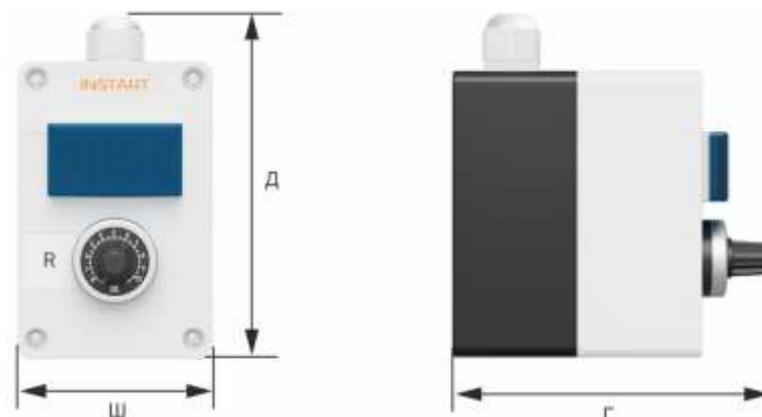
габаритные размеры ПУ-2-Х Y Z
